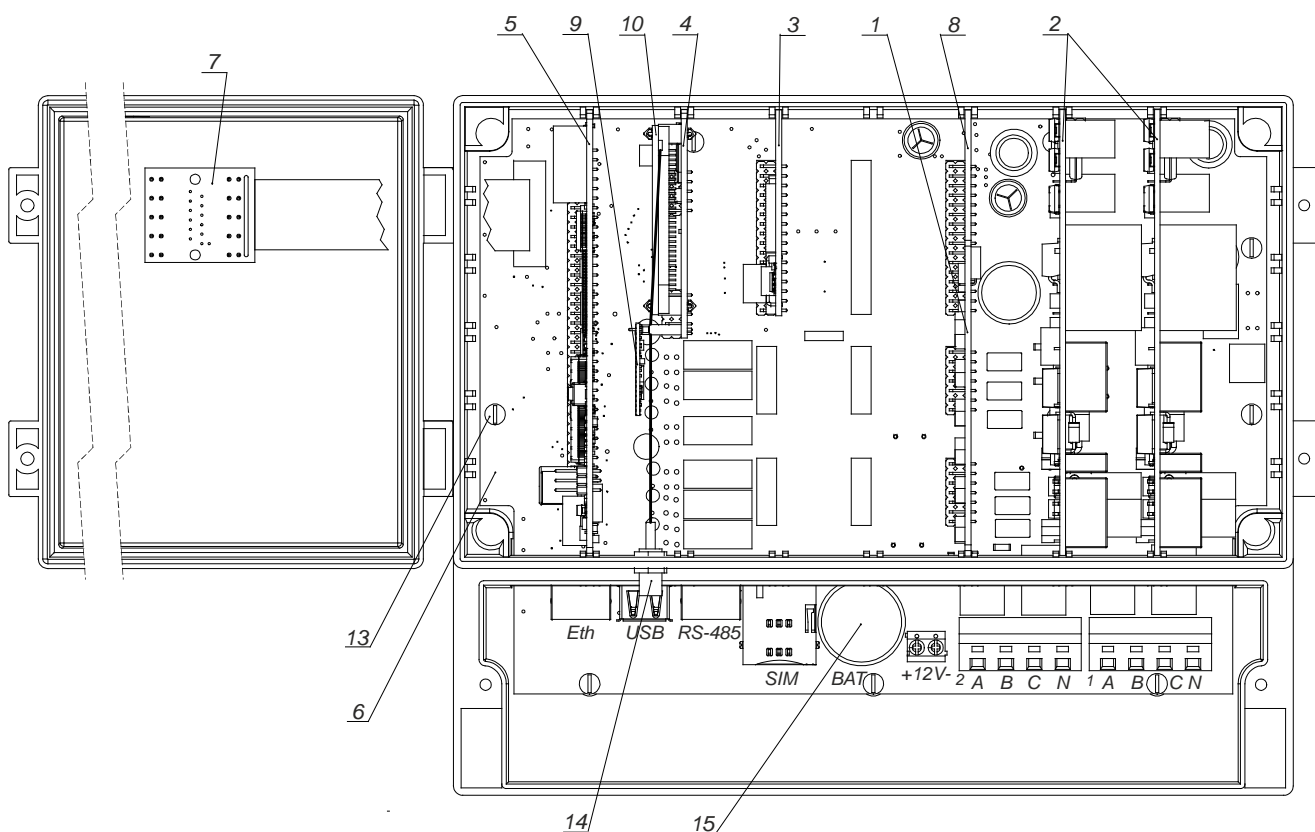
Внешний вид маршрутизатора с открытой лицевой крышкой
